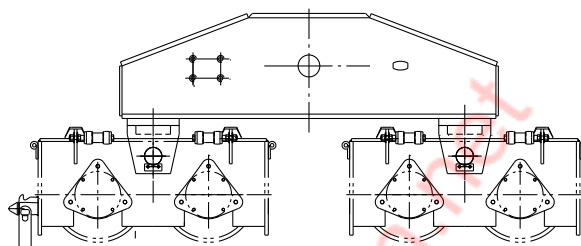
安装连接支座 Fig. 4-2 Fitting the connecting support
